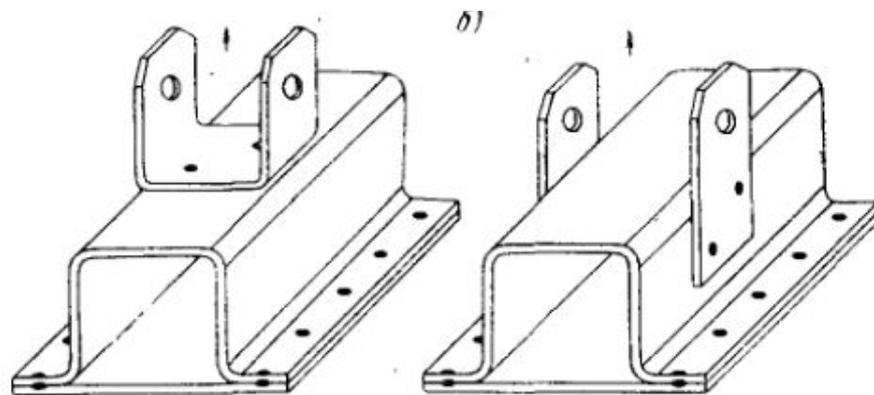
Детали, сваренные точечной сваркой:
